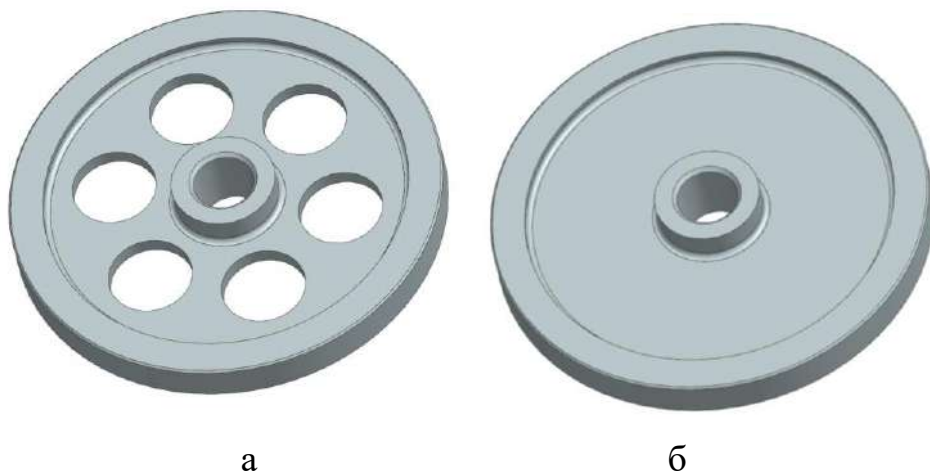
3D моделі деталі (а) та заготовки (б)
